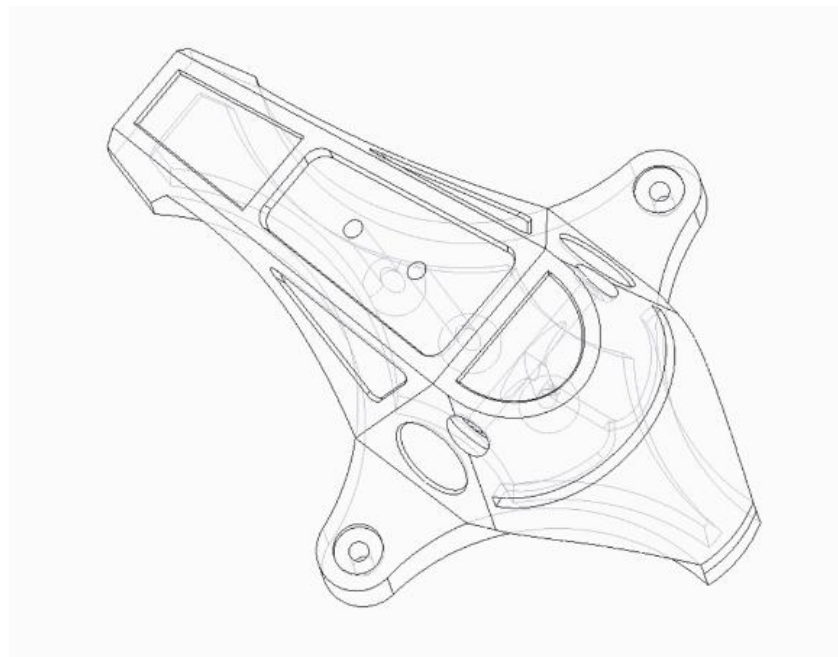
Каркасный вид матрицы для вакуумной формовки
